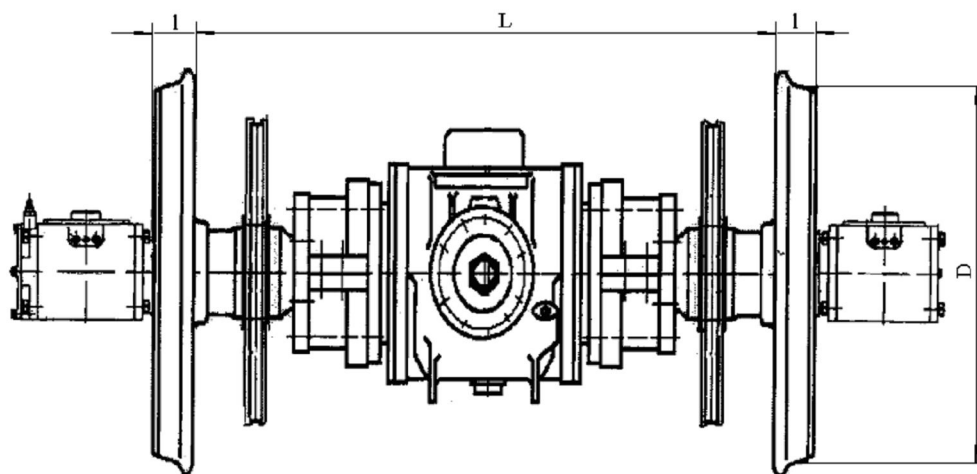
Колесная пара типа РВЗШ-957-П с буксовыми узлами, тормозными дисками «Кнопг-Времсе» и редуктором, изготавливаемая ОАО «ТВЗ»
